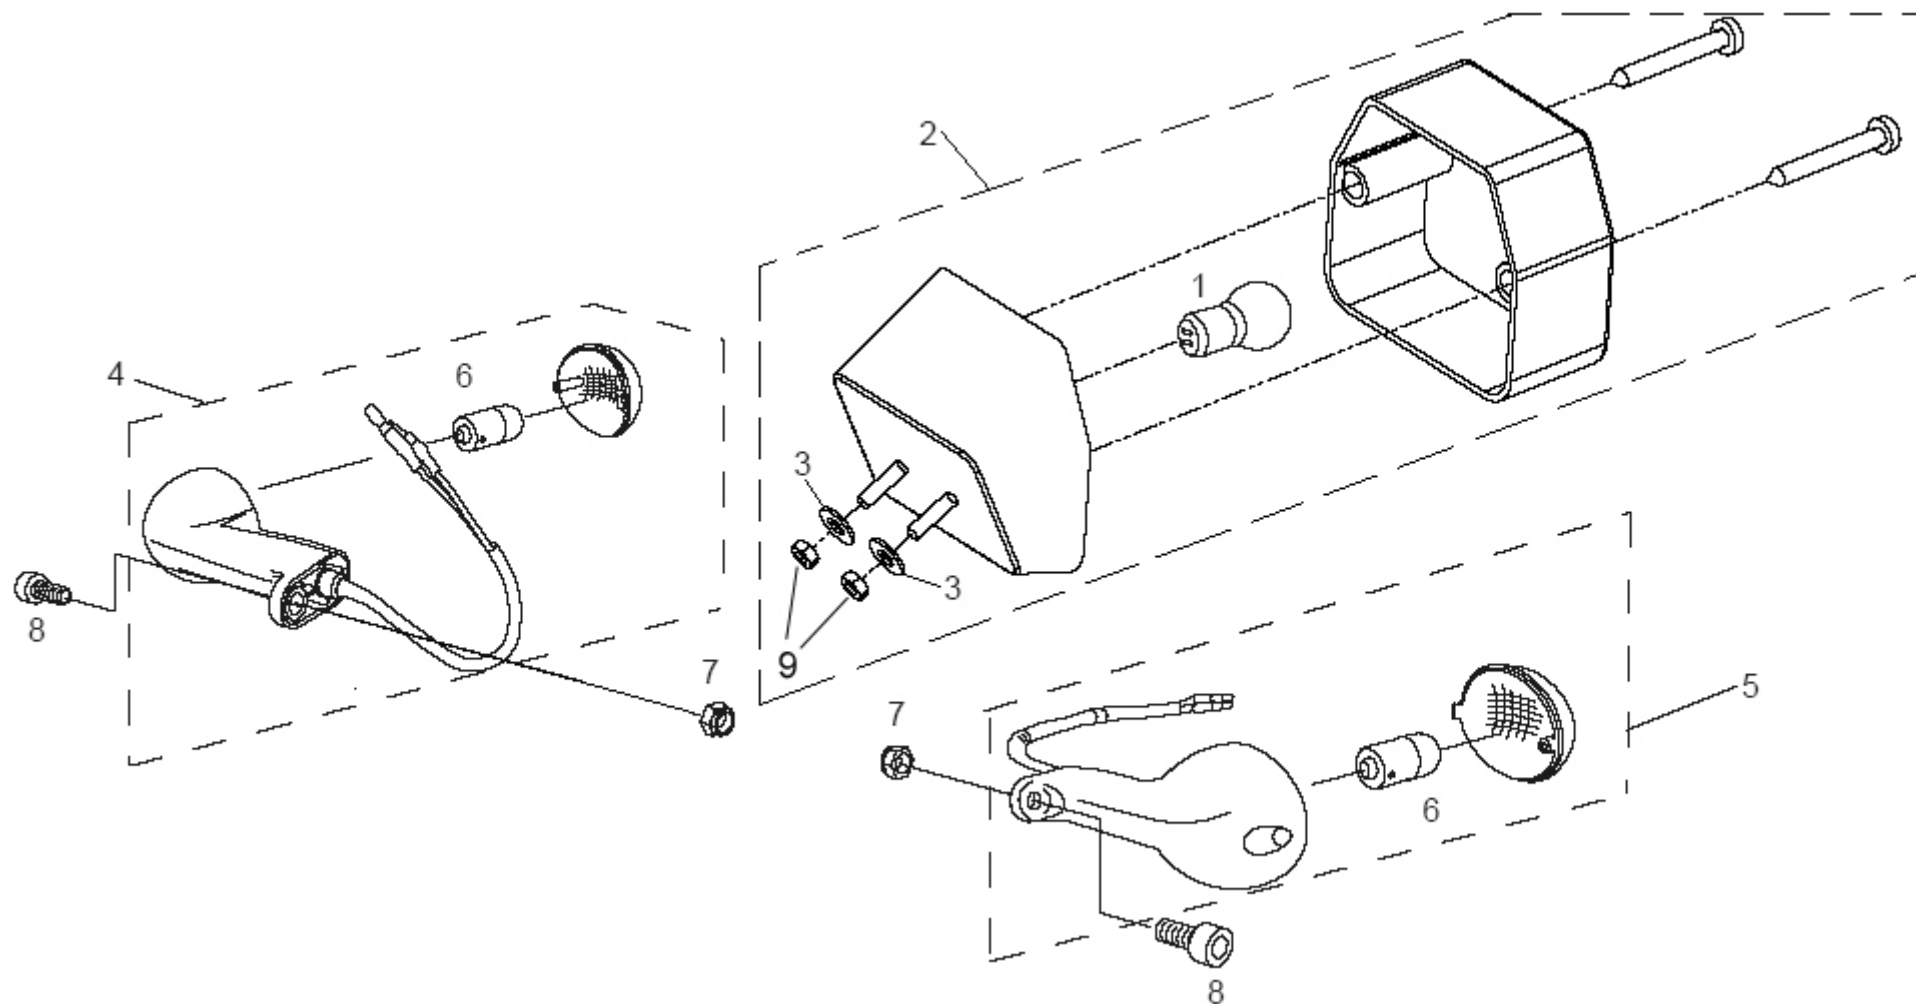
FEU ARRIÈRE / REAR LIGHT / FARO TRASERO
